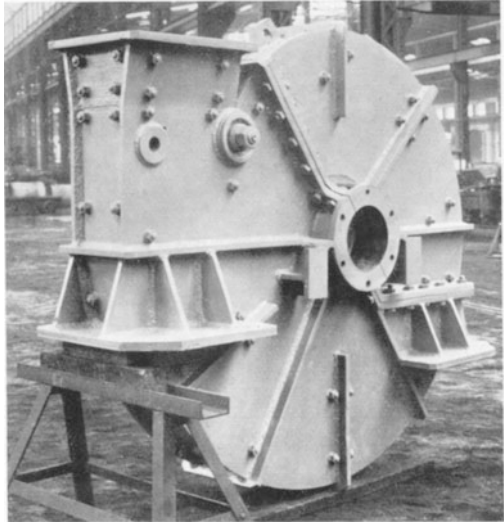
Gehäuse einer Baggerkreiselpumpe.
